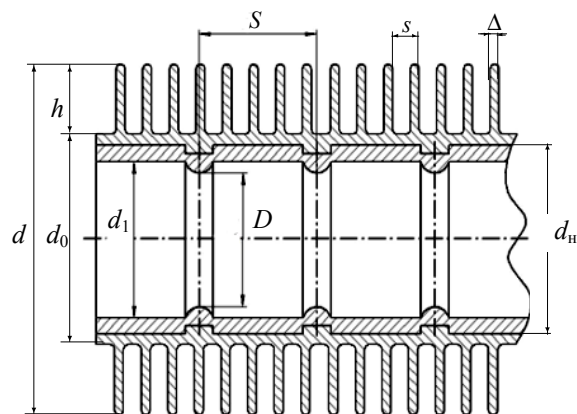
Биметаллическая ребристая труба с поперечной кольцевой накаткой на поверхности несущей трубы
